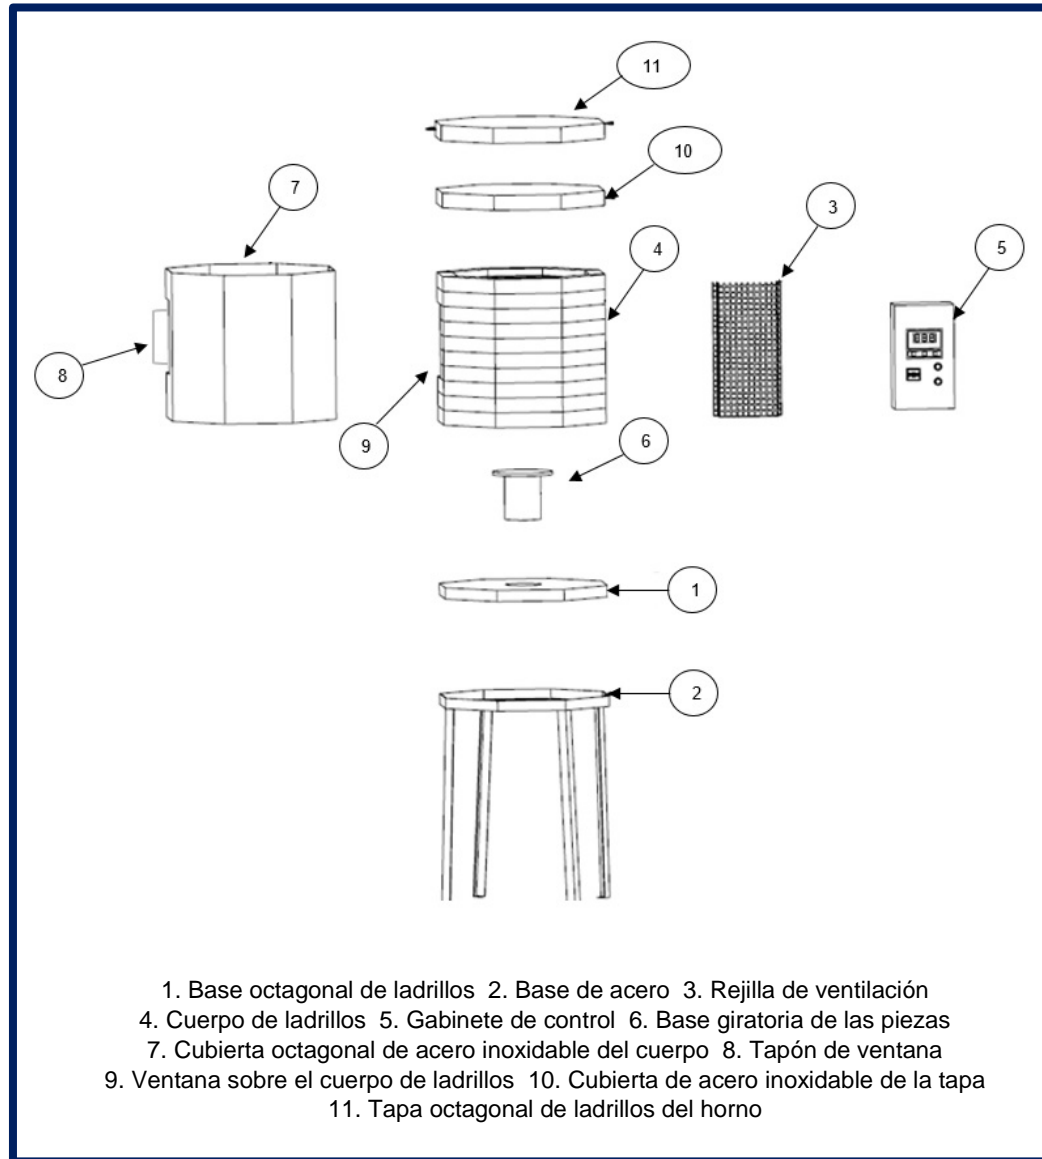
Vista explosionada de los componentes principales del horno eléctrico.
